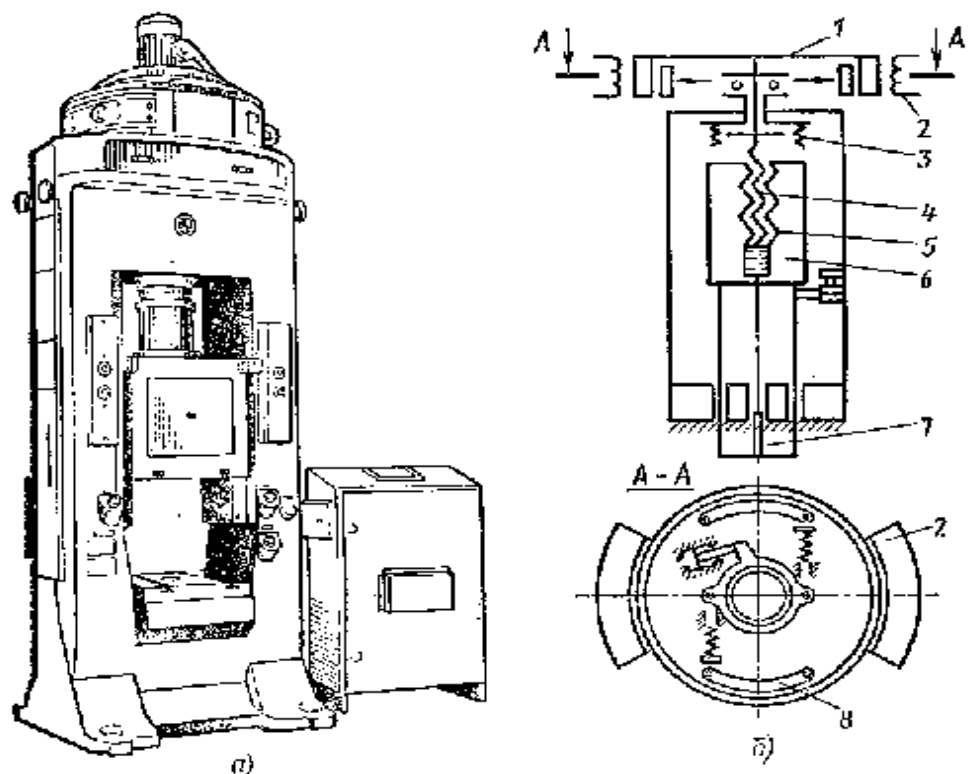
а - общий вид и б схема дугостаторного пресса: 1 – маховик; 2 – дугостаторы; 3 – станина с амортизаторами; 4 – винт; 5 – гайка; 6 – ползун; 7 – выталкиватель; 8 – тормоз
